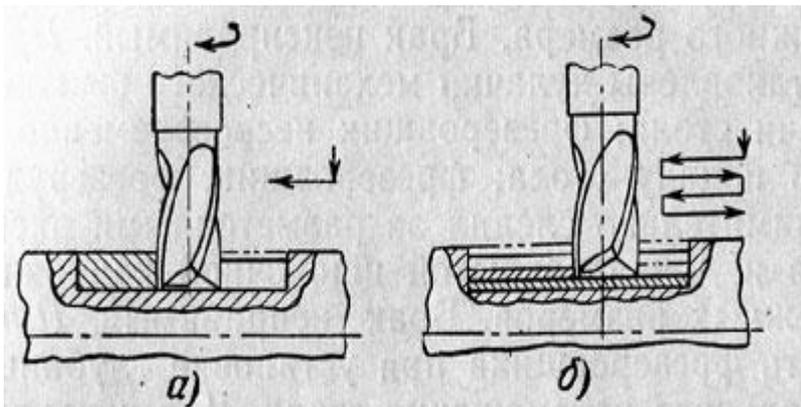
Схема подачи при фрезеровании шпоночной канавки:
